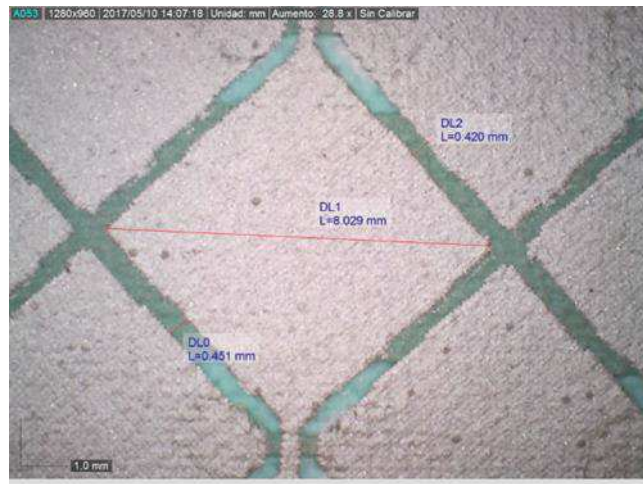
Detalles dimensionales del sensor D3.2-2. Fuente: propia.
